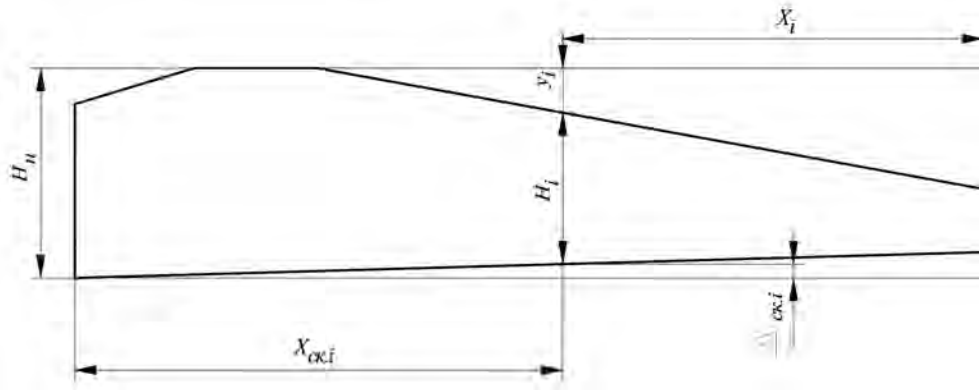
Схема для расчета калибровки планки стана ХПТР
